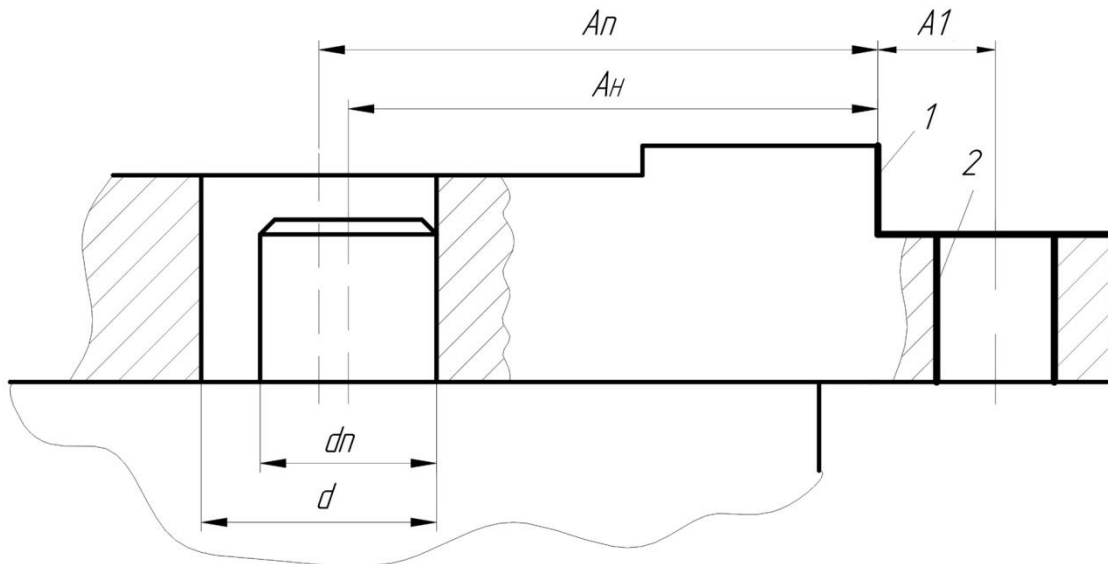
Установка заготовки по отверстию на цилиндрический палец
